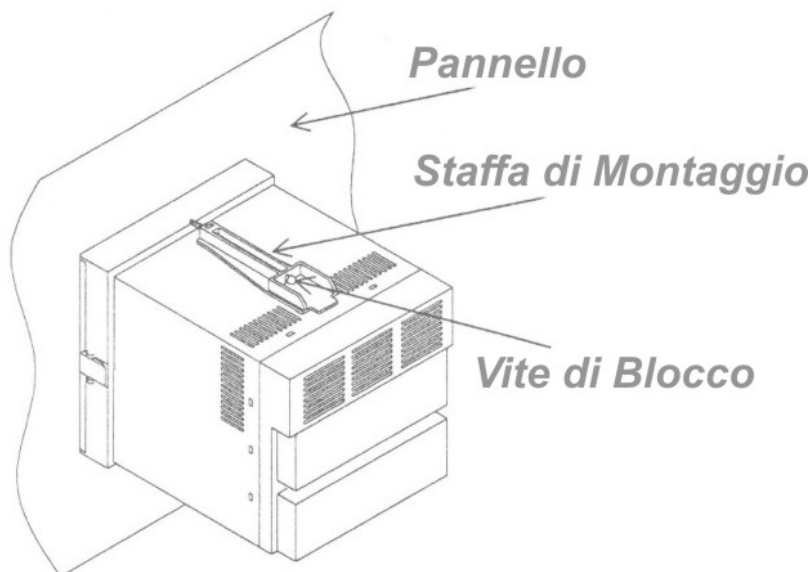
Vista Posteriore del Fissaggio a Pannello
